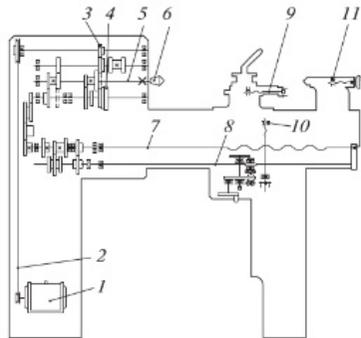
Кинематическая схема токарно-винторезного станка:
